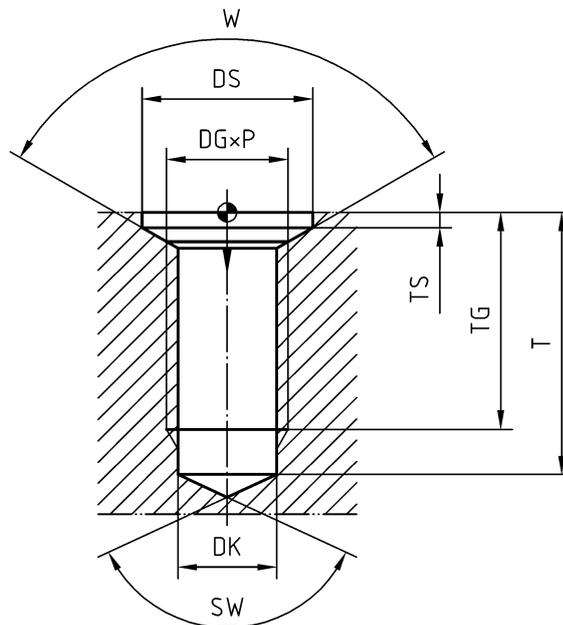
Gewindegrundbohrung mit Schutzsenkung
